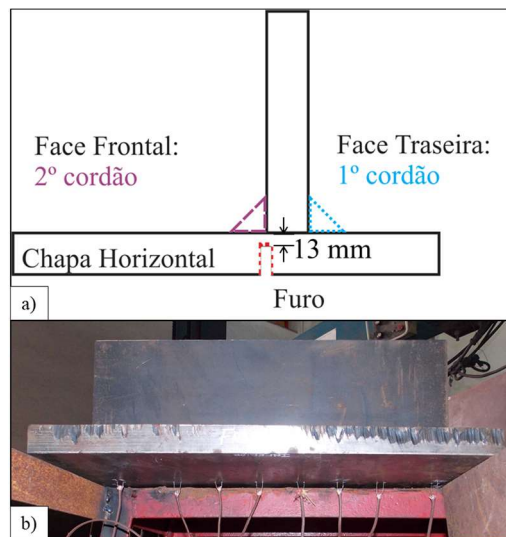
Instalação dos termopares. (a) corte transversal; (b) vista frontal, mostrando termopares soldados pela parte inferior da chapa horizontal.
